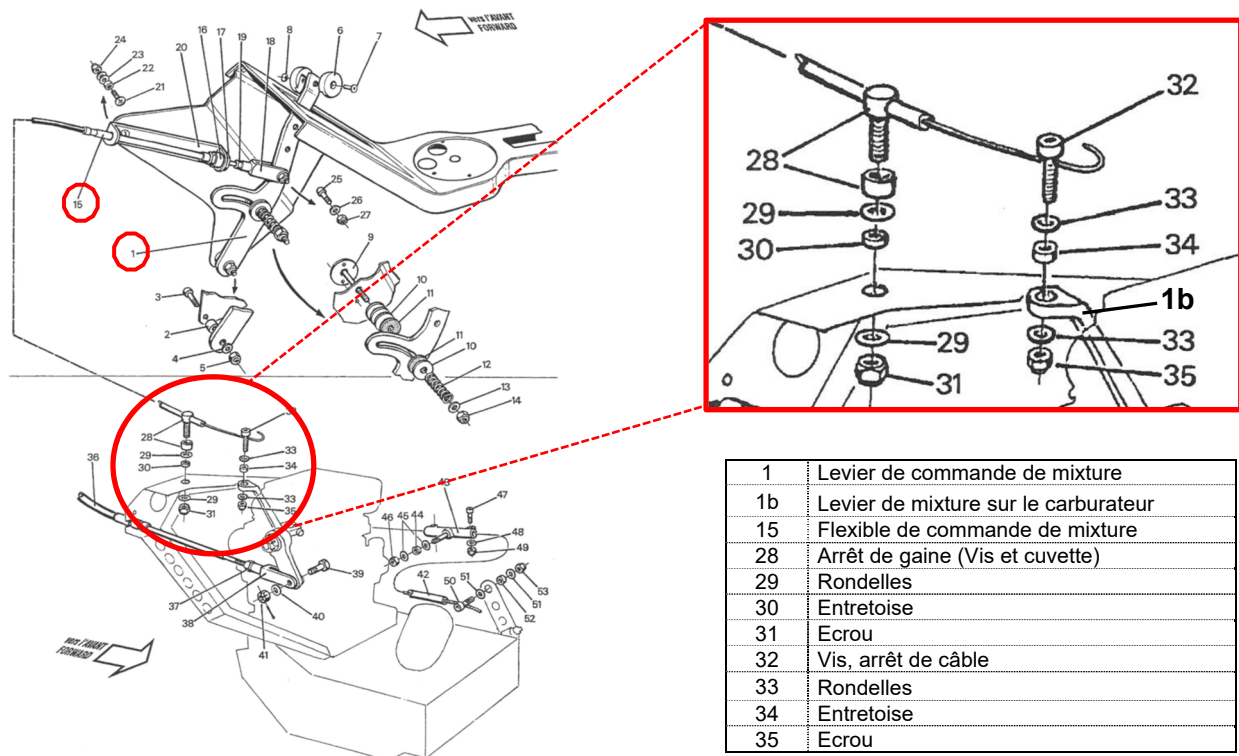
vue éclatée et détails du mécanisme du flexible de la commande de mixture, tirés de du catalogue de pièces illustrées (*Illustrated Part Catalog – IPC*) du Robin DR 400
